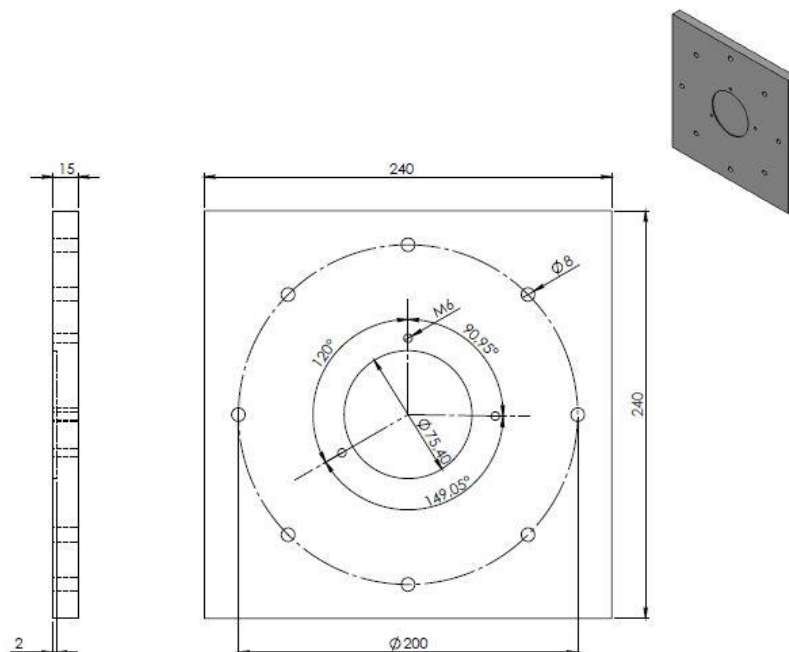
Dimensionamiento de la placa de unión con túnel
